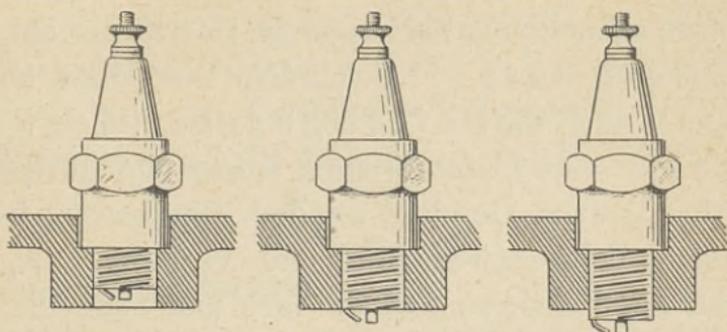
Richtige und falsche Gewindelänge der Zündkerze.
